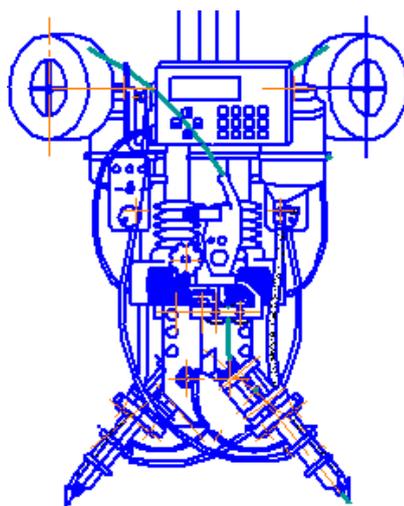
Сварочный автомат АДГ-630
